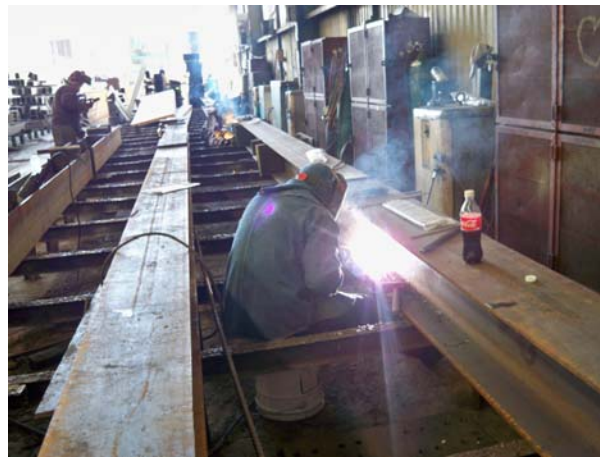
Preparación y ejecución de la soldadura
